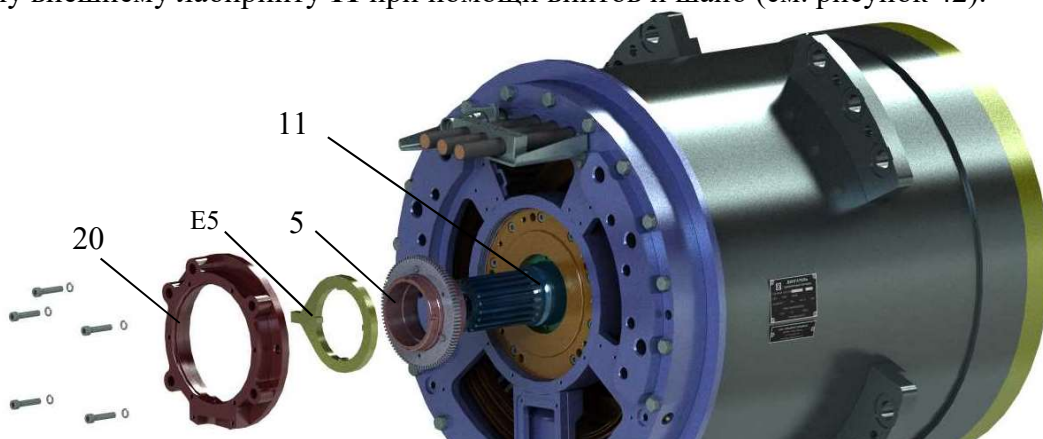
Монтаж упора с зубчатым диском и крышки датчика со стороны тормоза
